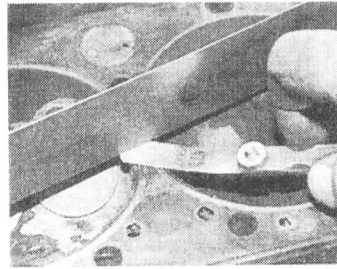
Проверить уплотнительную поверхность головки цилиндров на деформацию, приложив к ней линейку и попросив вставить под нее щуп (начните с щупа, толщина которого равна максимальной допустимой деформации уплотнительной поверхности).
